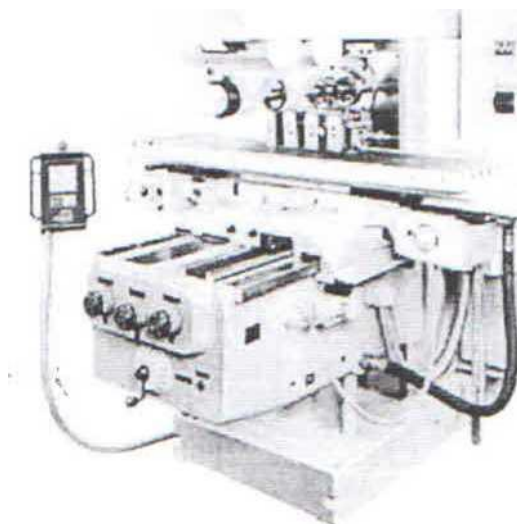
Горизонтальный консольно-фрезерный станок FU-350R
